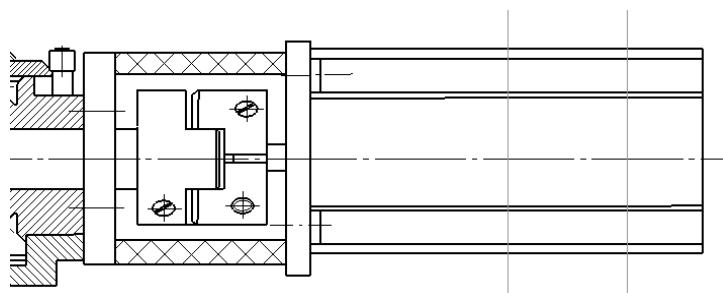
Схема під'єднання крокового двигуна до валу ділільної
